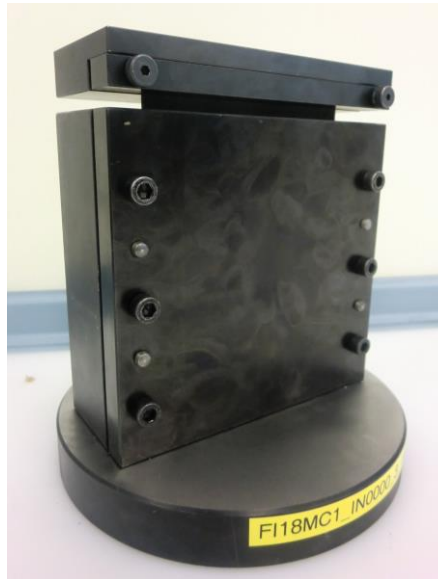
Imagen del útil de CAI desarrollado y fabricado
